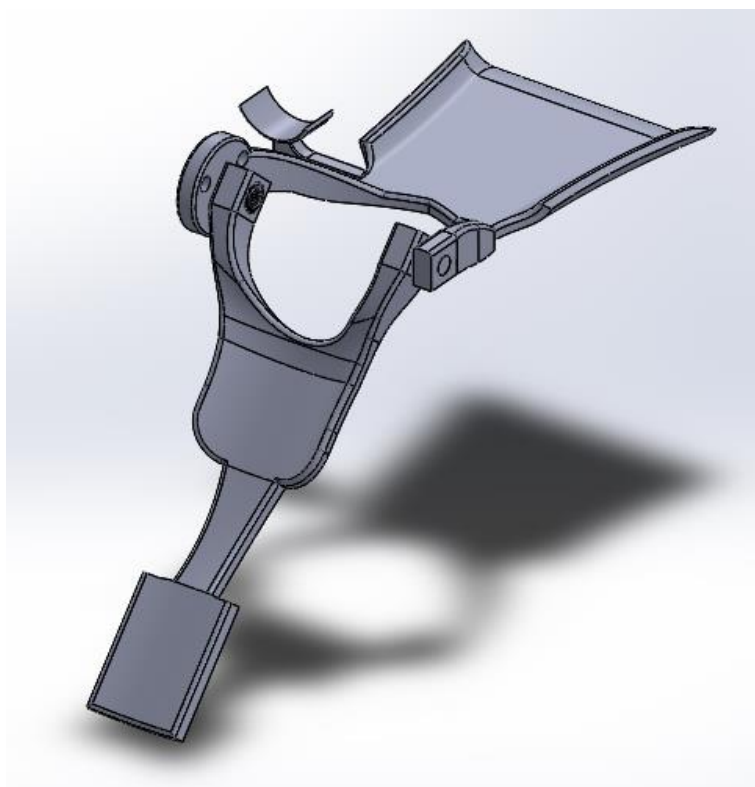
Vista isométrica del dispositivo. 60° de flexión de rodilla.
